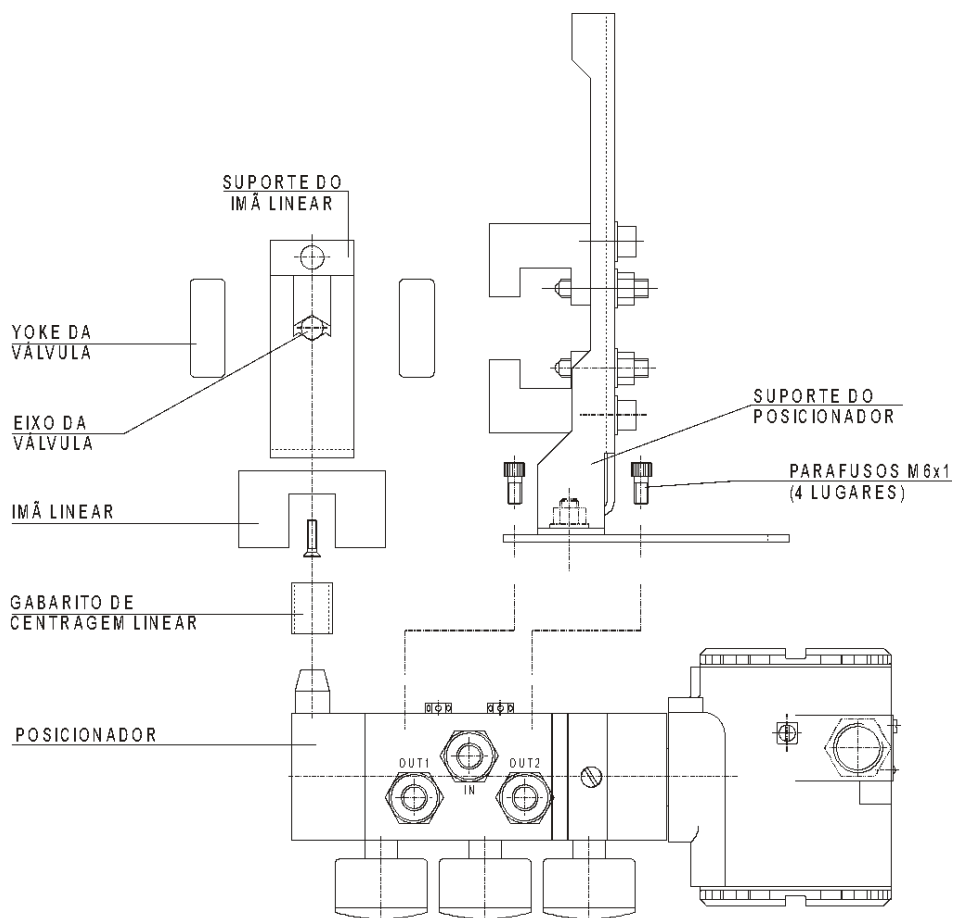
Esquema de Montagem do Posicionador em Atuador Linear
